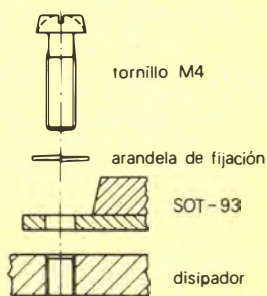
Montaje con tornillo directo en la carcasa del disipador.
